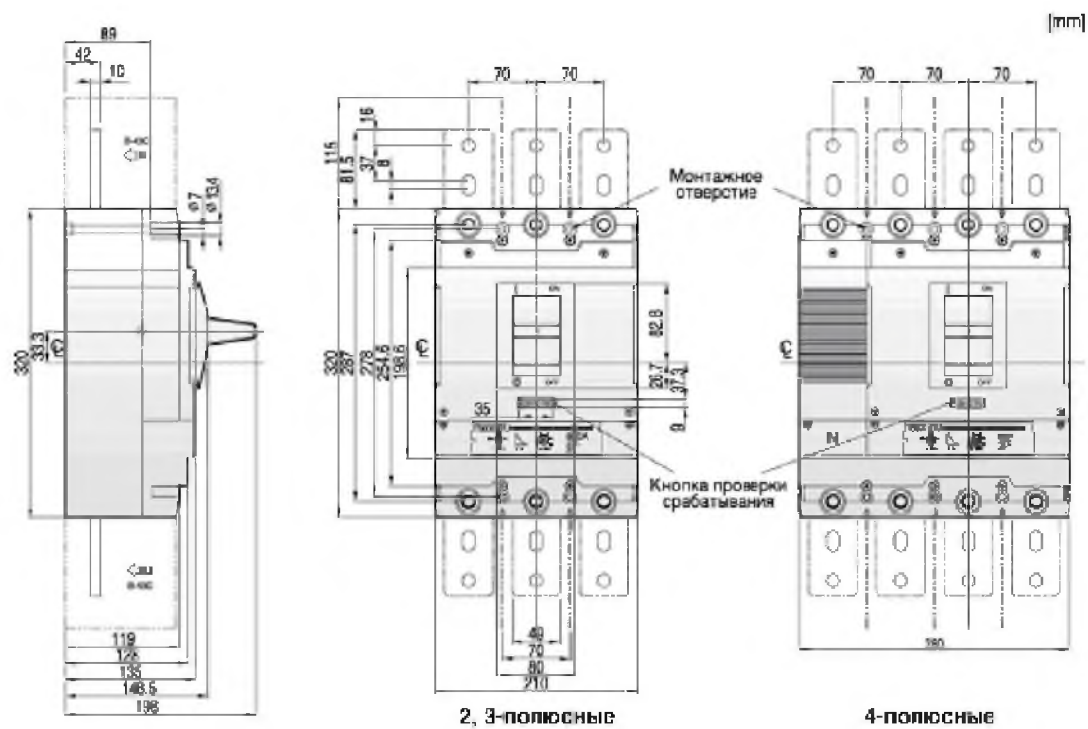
Габаритные и присоединительные размеры стационарных выключателей TS800
